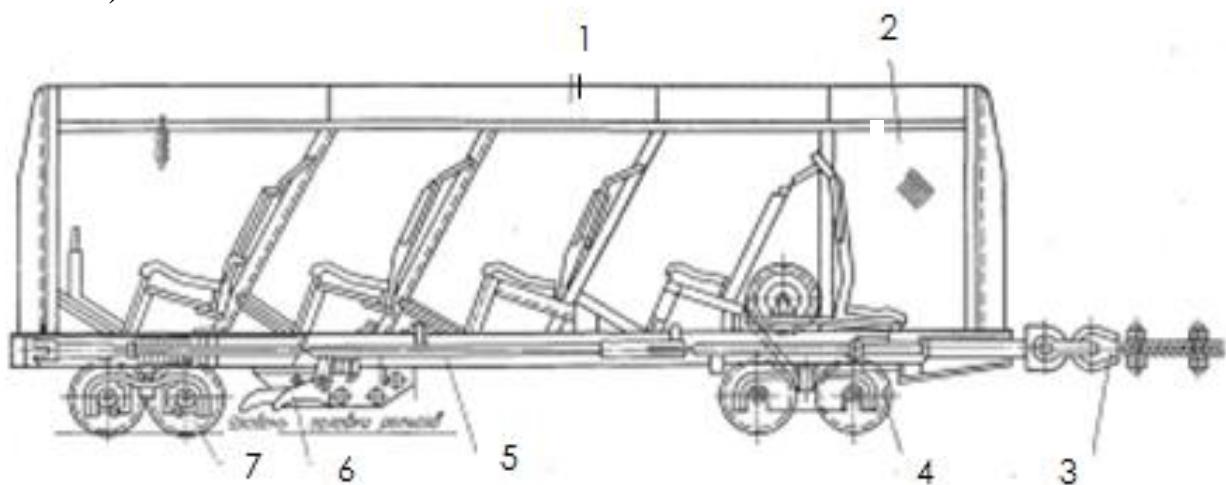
Вагонетка для перевозки людей по наклонным выработкам:
